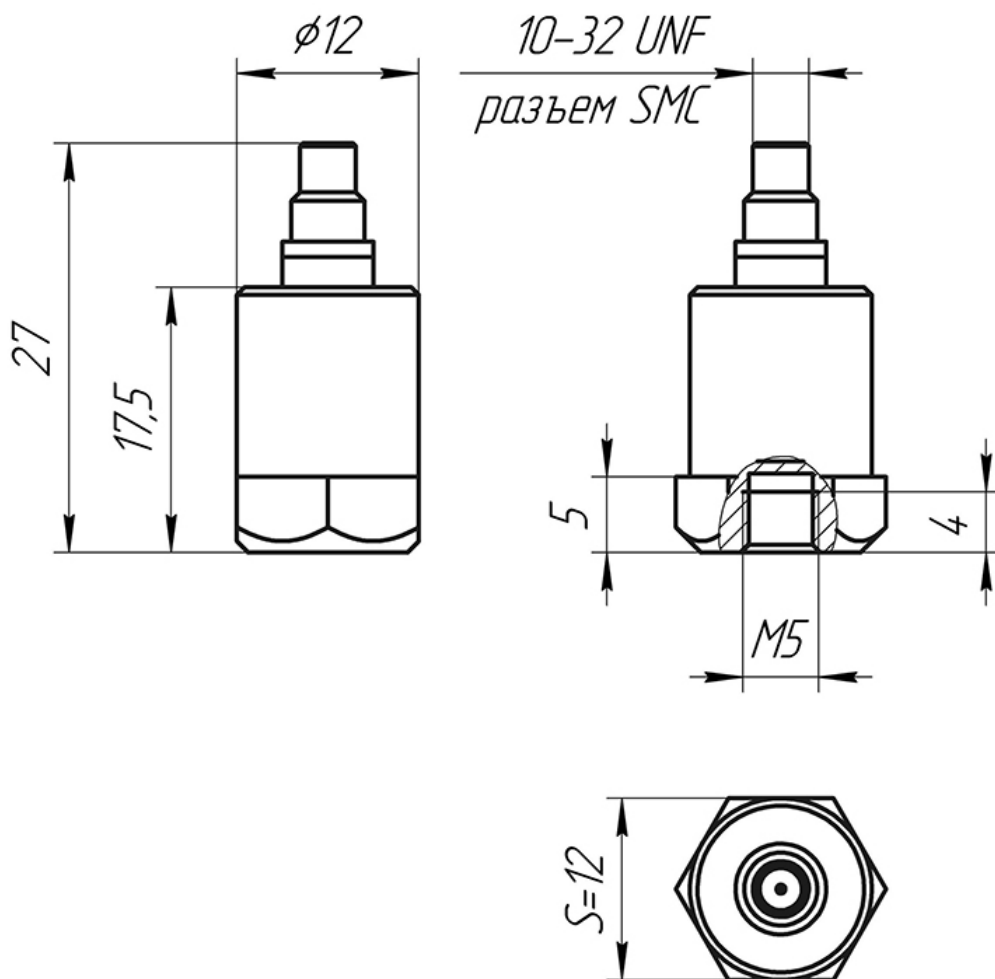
Габаритный чертеж акселерометра ВС 111 (вывод сверху)
